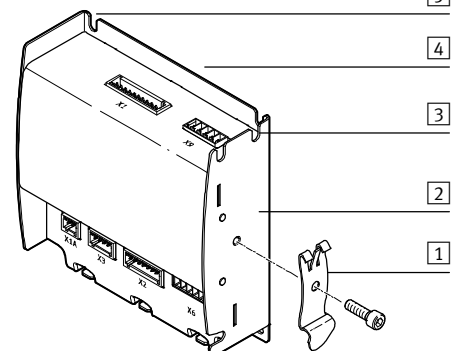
Монтаж на боковой или задней крепежной поверхности
